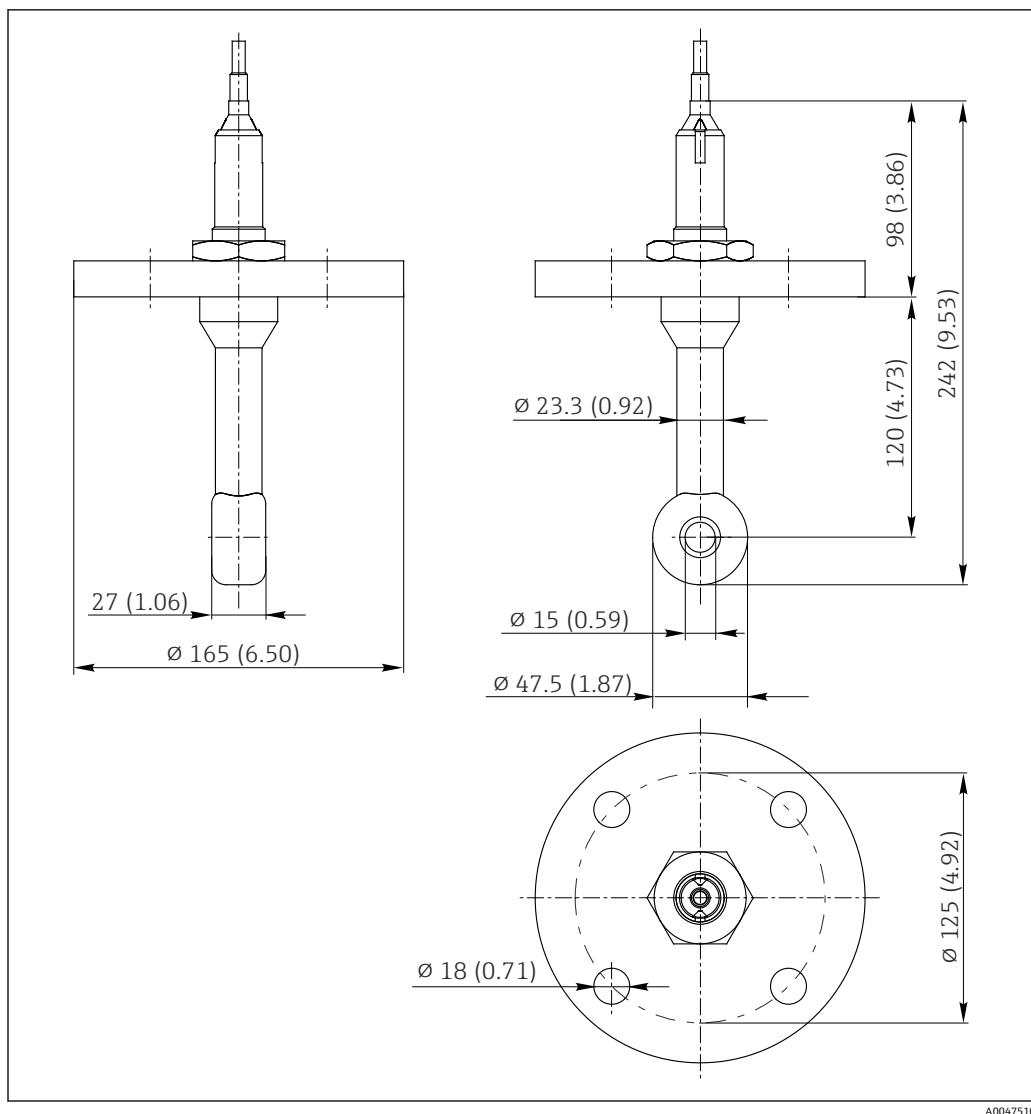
EN1092-1 DN50 PN16 法兰连接, PFA 型传感器采用 316L 焊接密封板。测量单位 mm (in)
